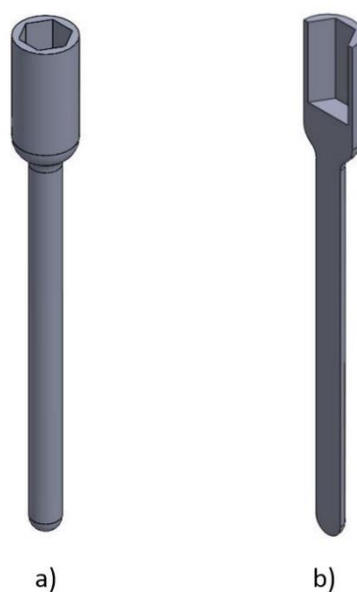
a) Vista Isométrica da Caneta; b) Vista em Corte da Caneta
